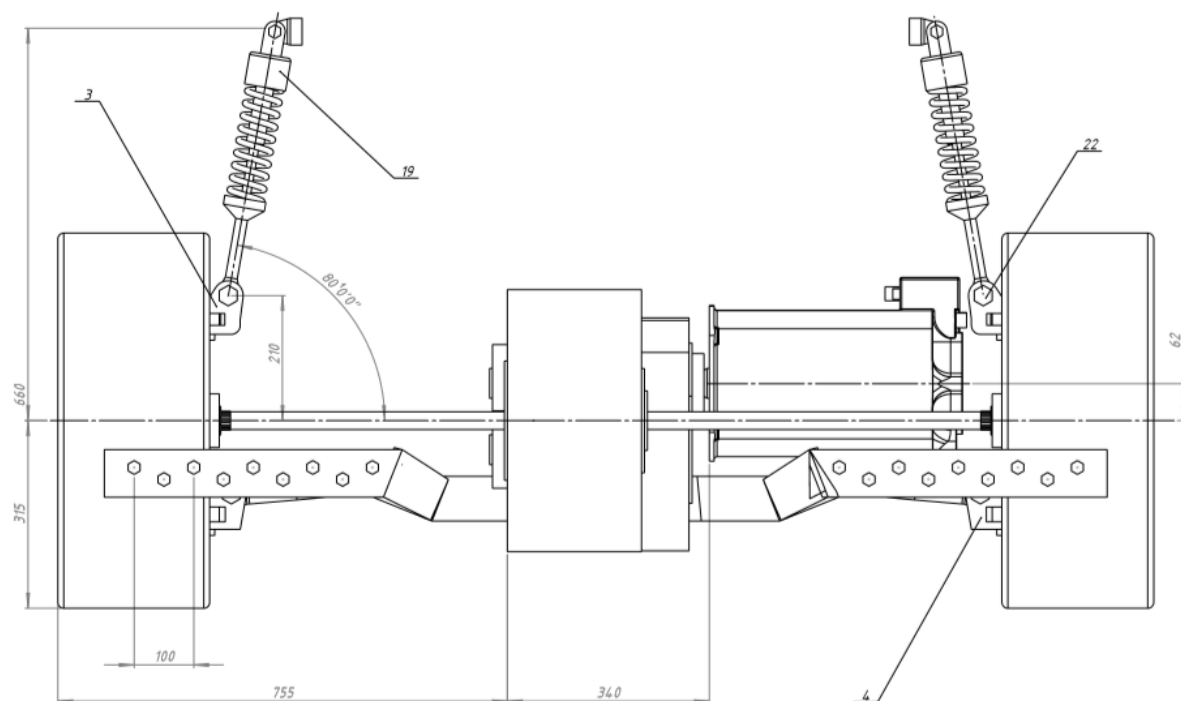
Загальний вигляд заднього приводу(Вид спереду).
